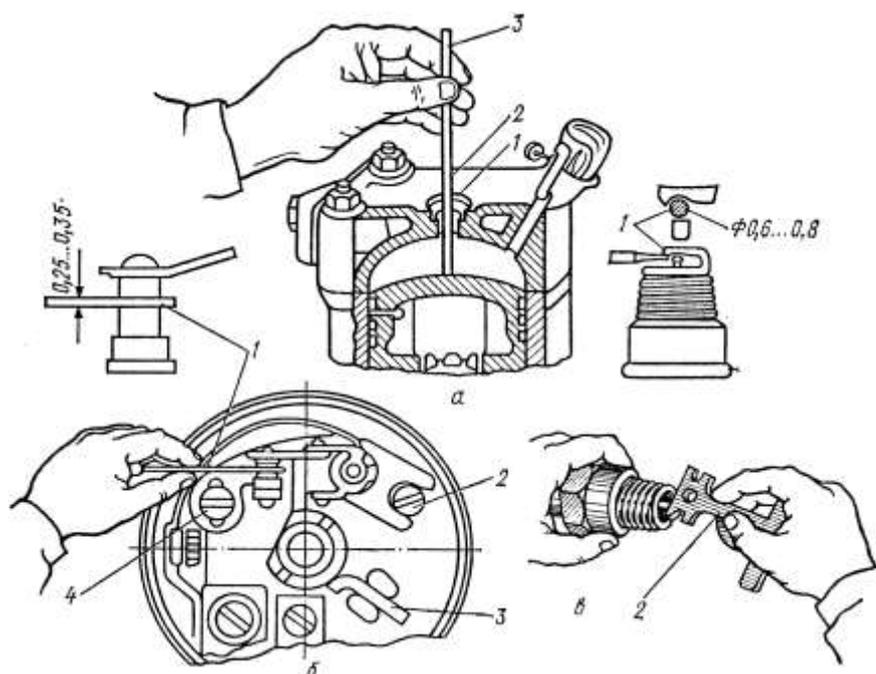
Проверка и регулировка электрооборудования пускового двигателя
